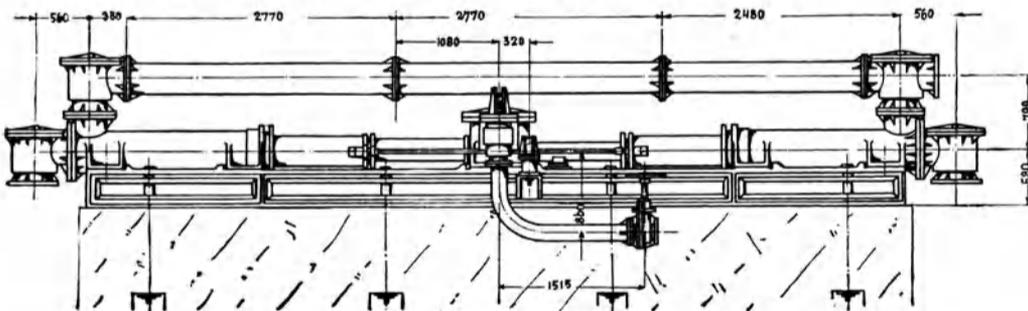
Hydraulische Fördermaschine. Maßstab 1:180.
